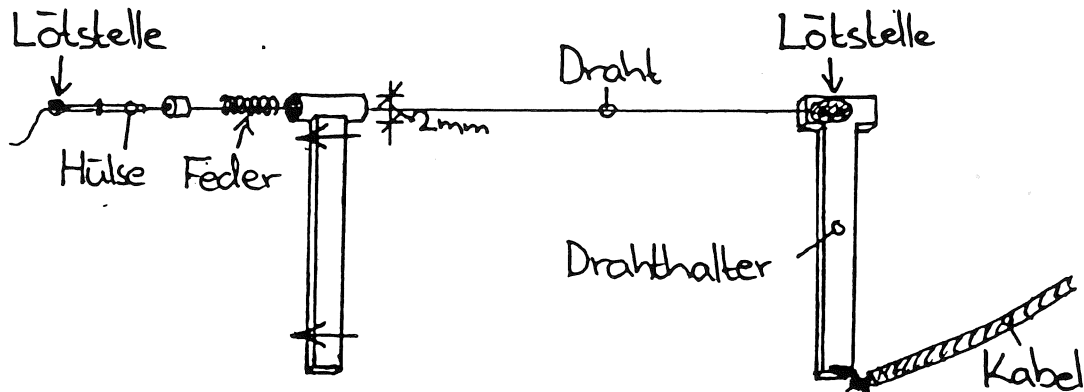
"Befestigung der Drähte. Die Drahthalter bestehen aus Epoxy, das einseitig mit einer Kupferschicht beschichtet ist."
